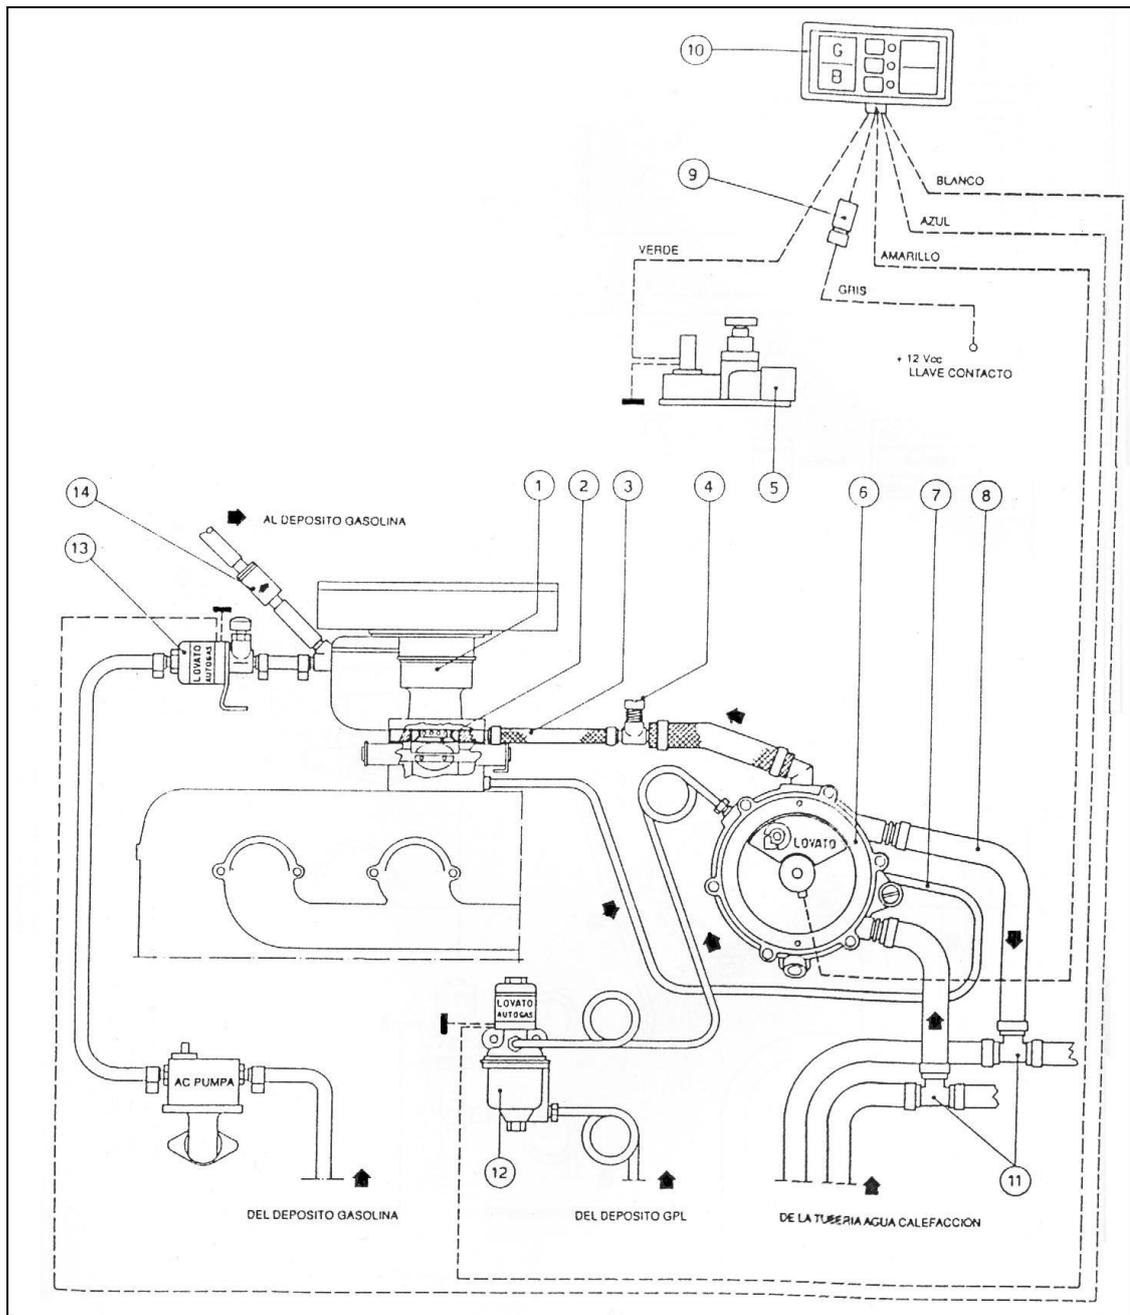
Esquema de montaje del reductor en vehículos a carburador
